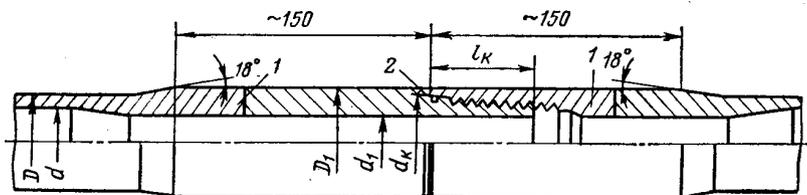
Насосно-компрессорные трубы с приваренными замками, используемые в качестве бурильных труб малого диаметра (по стандартам АНИ). 1 — сварной шов; 2 — уплотнительное кольцо
